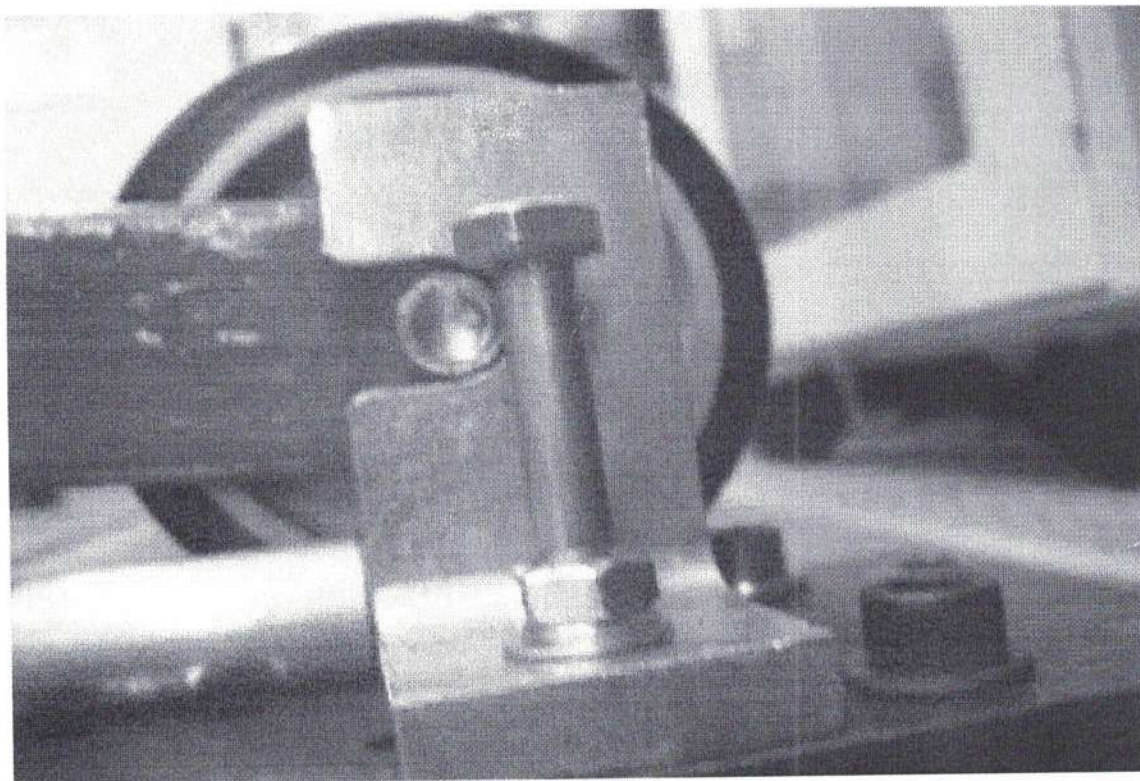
Foto 4 Lado direito da amostra 1 após ensaio.
